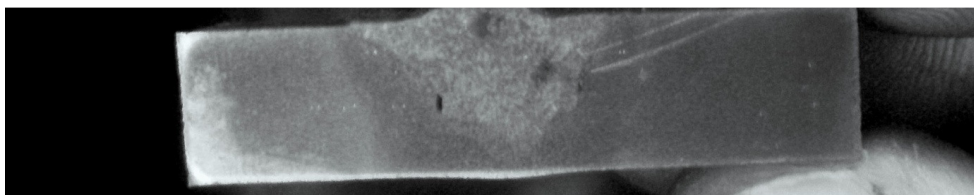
62 - Amostra do provete 2 (soldadura com vibração).
